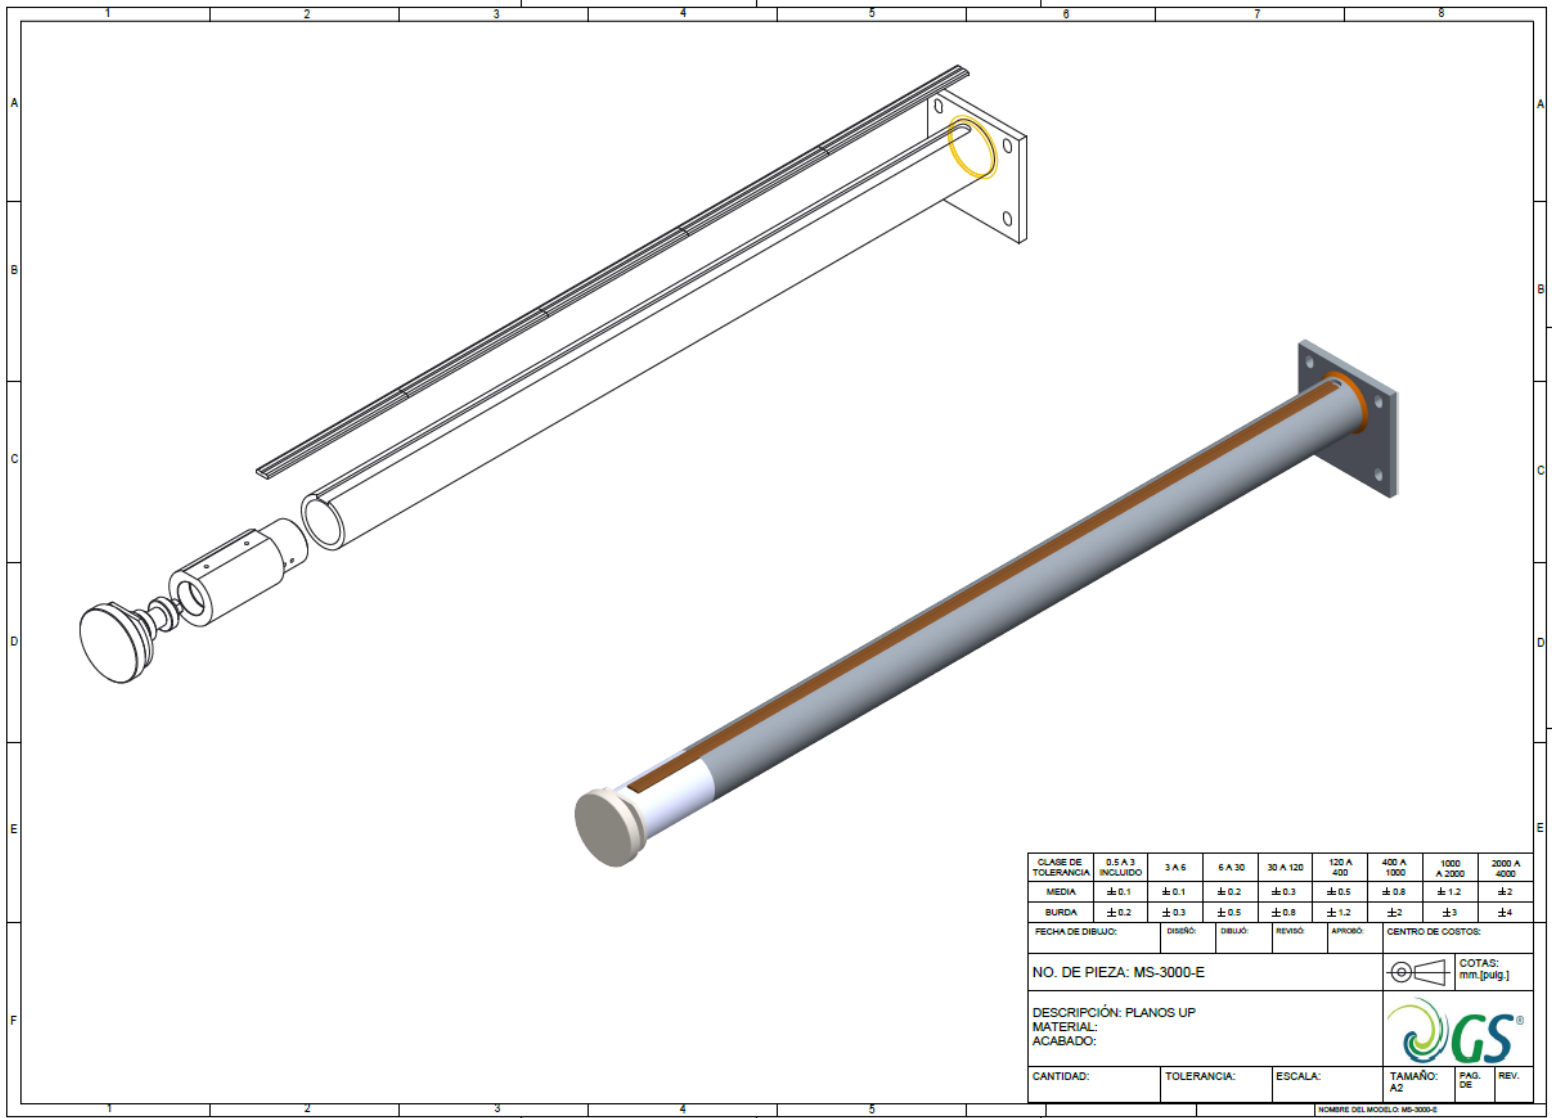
Plano de ensamble para el mandril de soporte de soldadura lineal, mostrando sus componentes (Cortesía de Green Spare).
